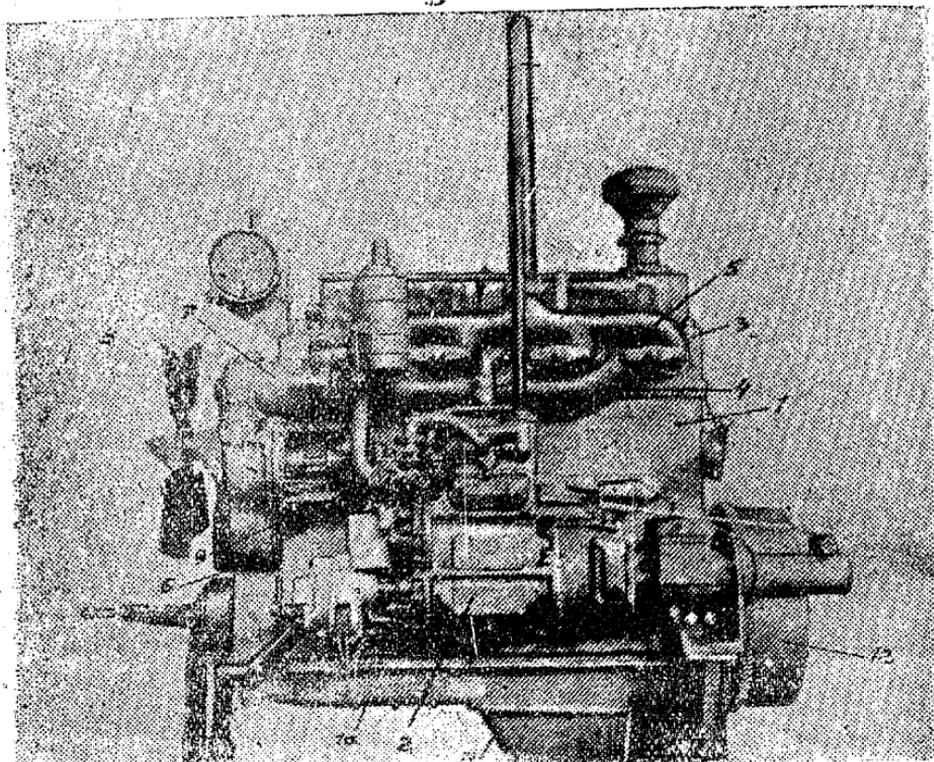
Общий вид газового двигателя МГ—17 слева: 1—блок-картер; 2—пусковой двигатель; 3—головка блока; 4—всасывающая труба; 5—выхлопная труба; 6—кожух шестерен распределения; 7—динамо; 8—вентилятор; 9—водяной насос; 10—нижний картер; 11—поддон; 12—маховик.
